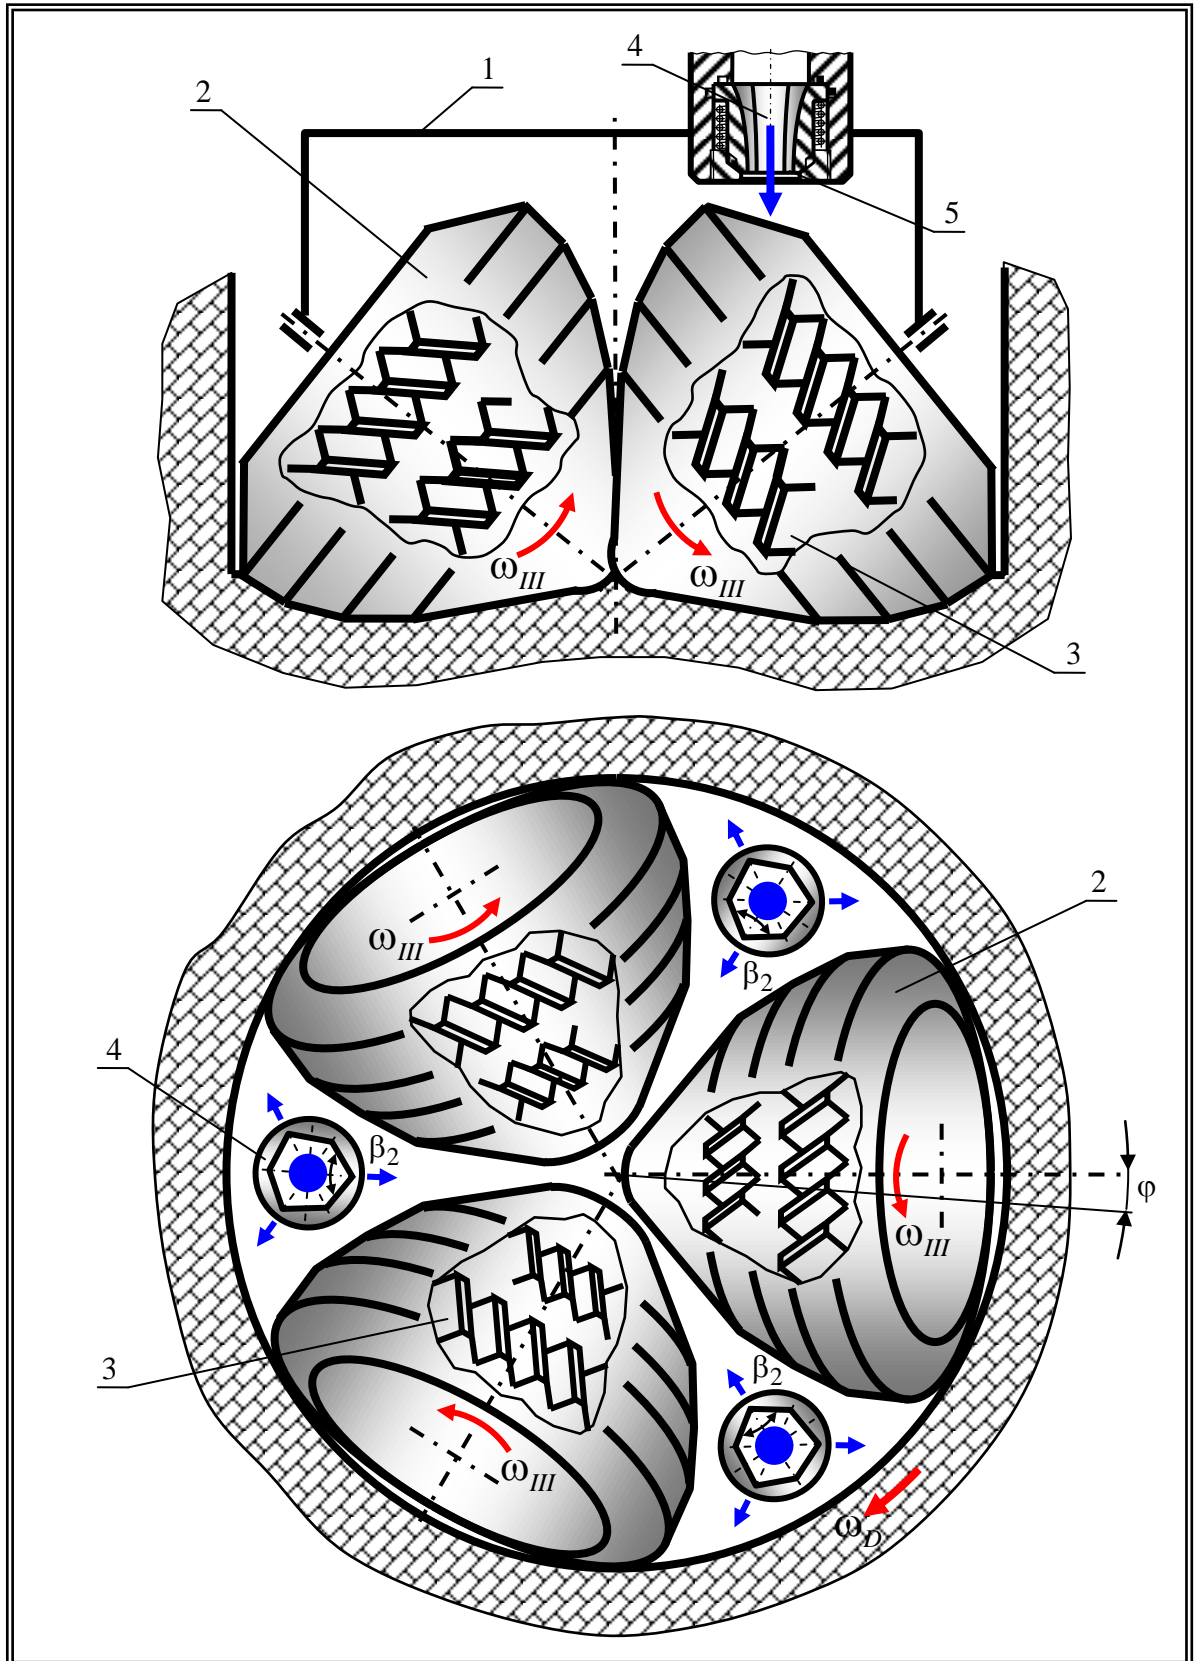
Схема шарошечного бурового долота, оснащенного боковыми гидромониторными узлами новой конструкции
